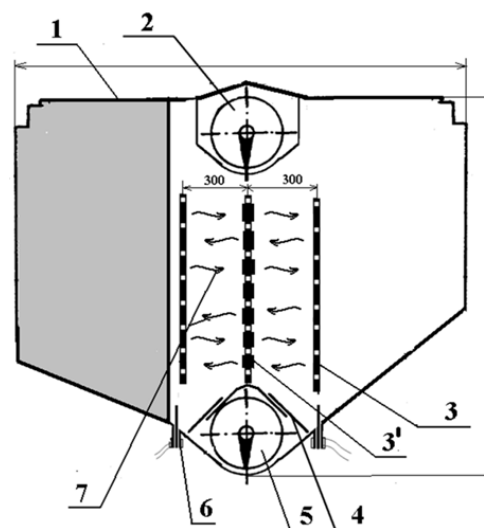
Бункер зерноуборочного комбайна с электромагнитными излучателями (вид в разрезе сбоку): 1 – корпус бункера, 2 – загрузочное устройство, 3 – панель с излучателями, 3' – панель с двусторонними излучателями, 4 – система регулировки подачи при разгрузке, 5 – выгрузной шнек, 6 – дополнительная система регулировки подачи при разгрузке, 7 – направление основного потока излучения
